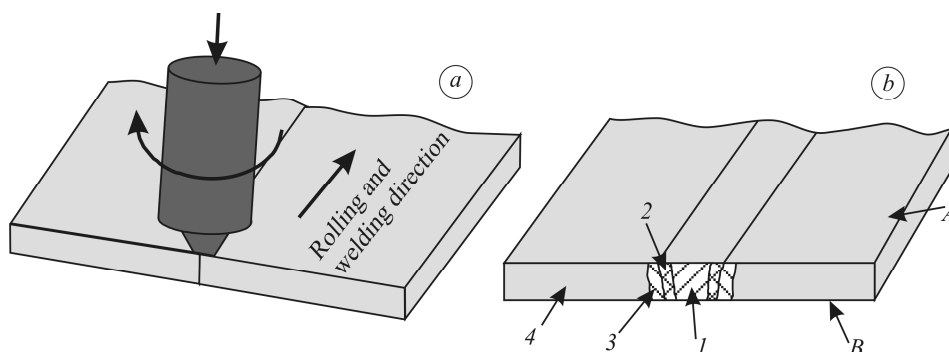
Схеми ЗТП (a) і різних зон з'єднання (b): 1 – МШ; 2 – ЗТМБ; 3 – ЗТВ; 4 – ОМ; А – лицева поверхня; В – тильна.
